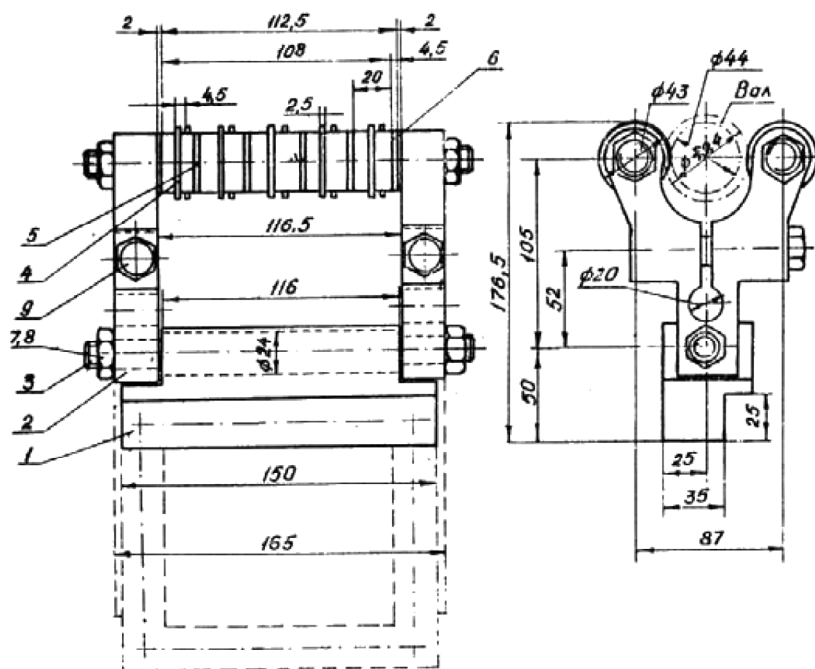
Обкатник для упрочнения канавок вторичного вала коробки передач
